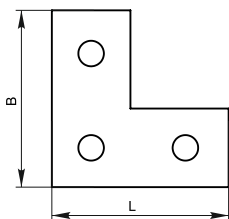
Пластина соединительная L-образная для STRUT-профиля
